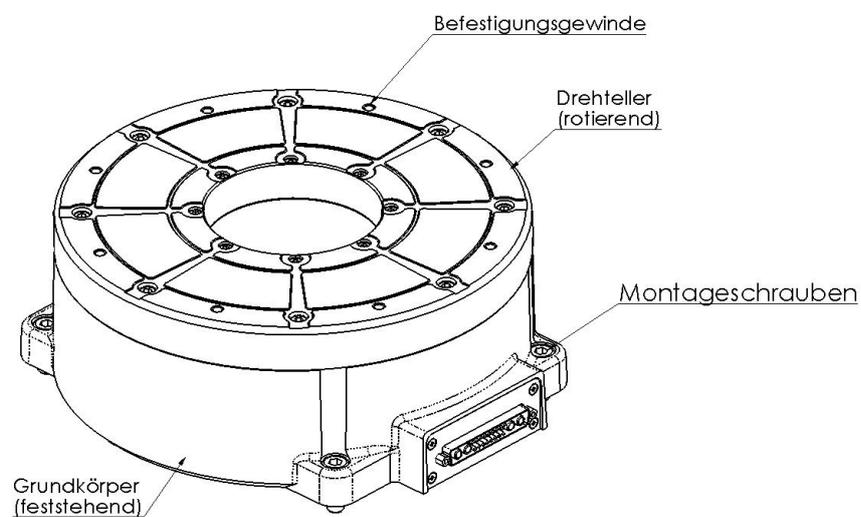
Befestigungsvorschrift Torquemotor iTM 180-240
